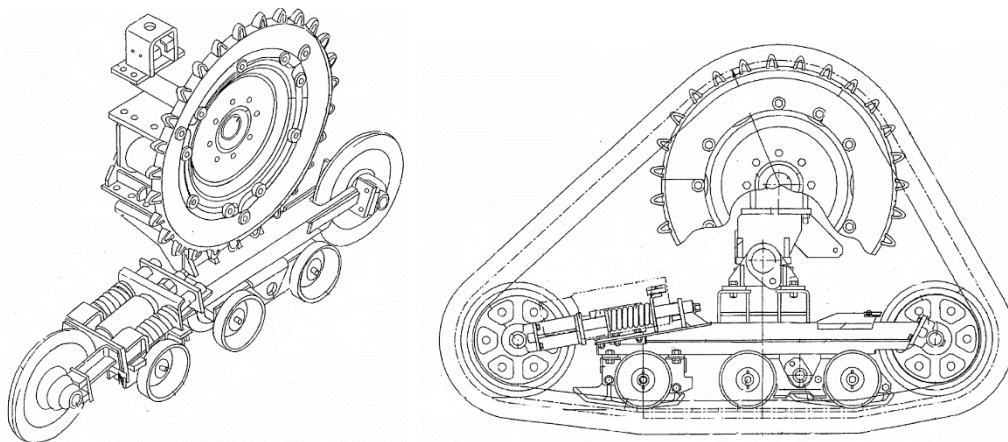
Внешний вид конструкции патента EP 2103508 B1
